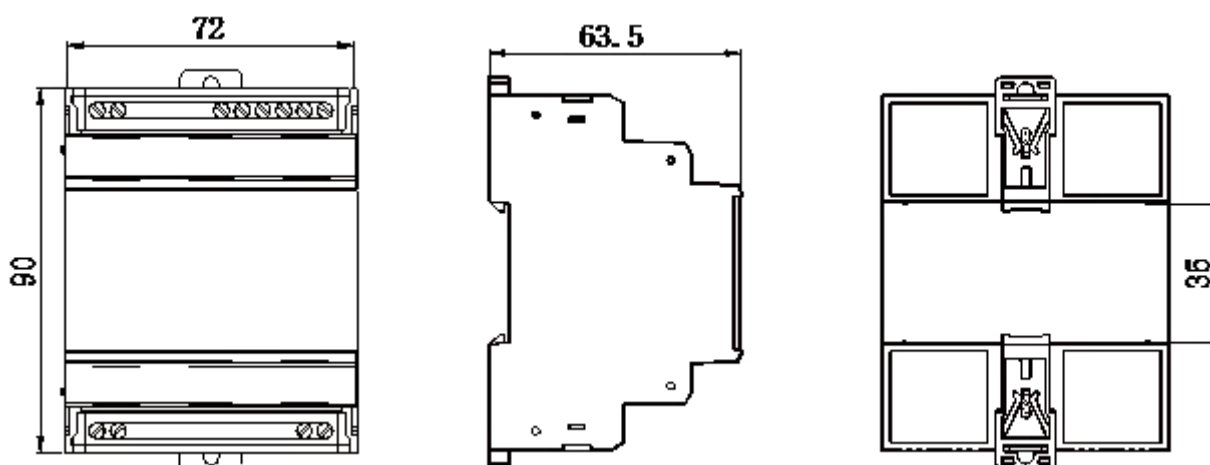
Внешний вид и габаритные размеры приборов КСМ-М2
